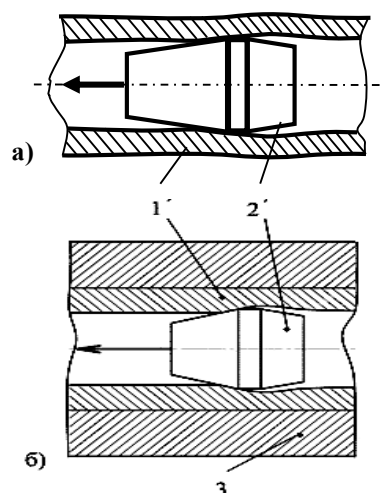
Технологічні схеми ДП: а) без обмеження радіальної деформації зовнішньої поверхні; б) з обмеженням, в жорсткій обоймі; 1 – заготовка; 2 – інструмент; 3 – жорстка обойма
